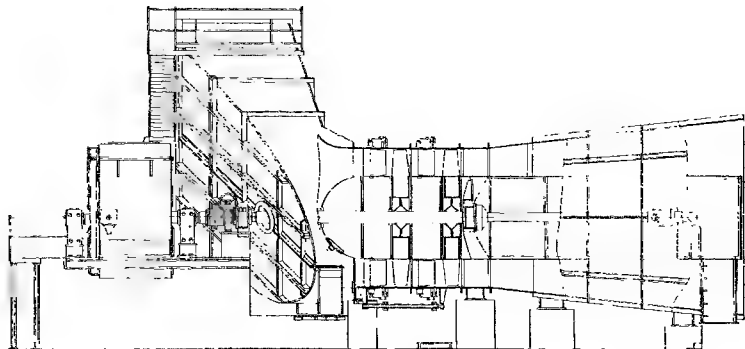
13 Осевой компрессор БКЗ ДО-31.5
